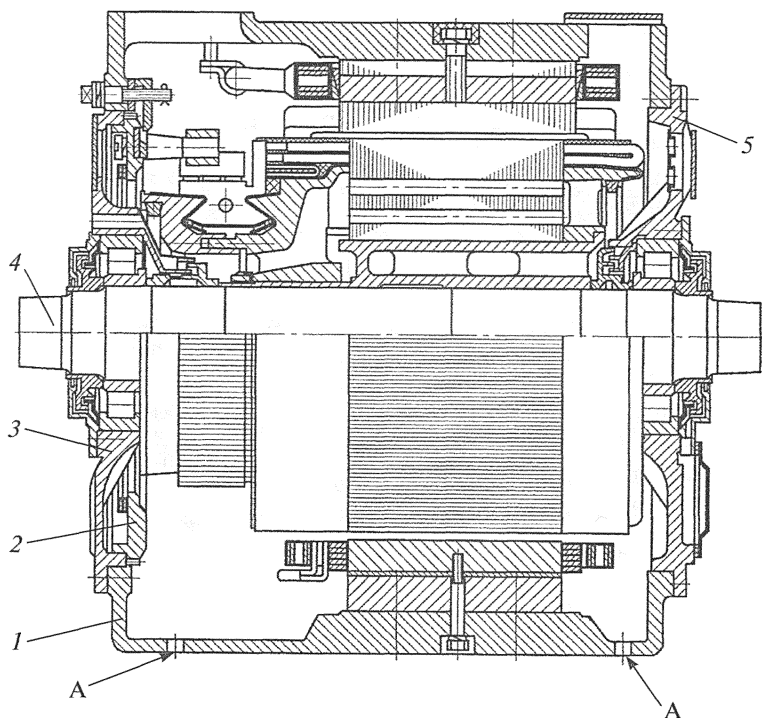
Продольный разрез тягового двигателя НБ-514Е:
